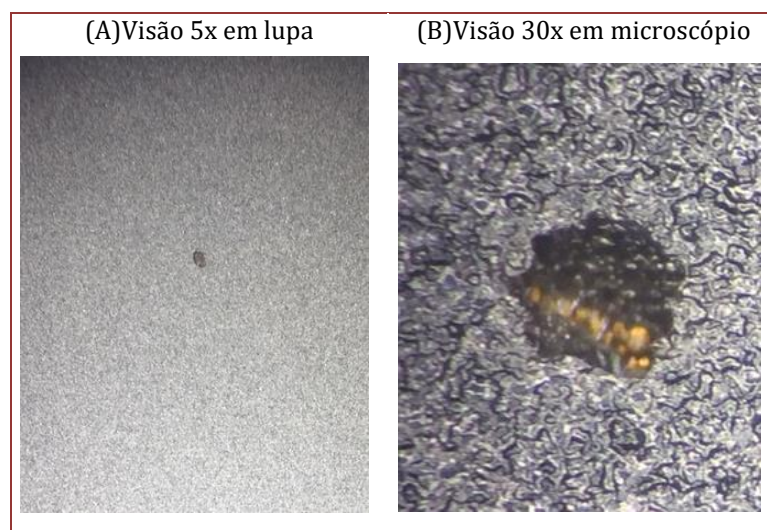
Buracos externos durante o encapsulamento do BGA
